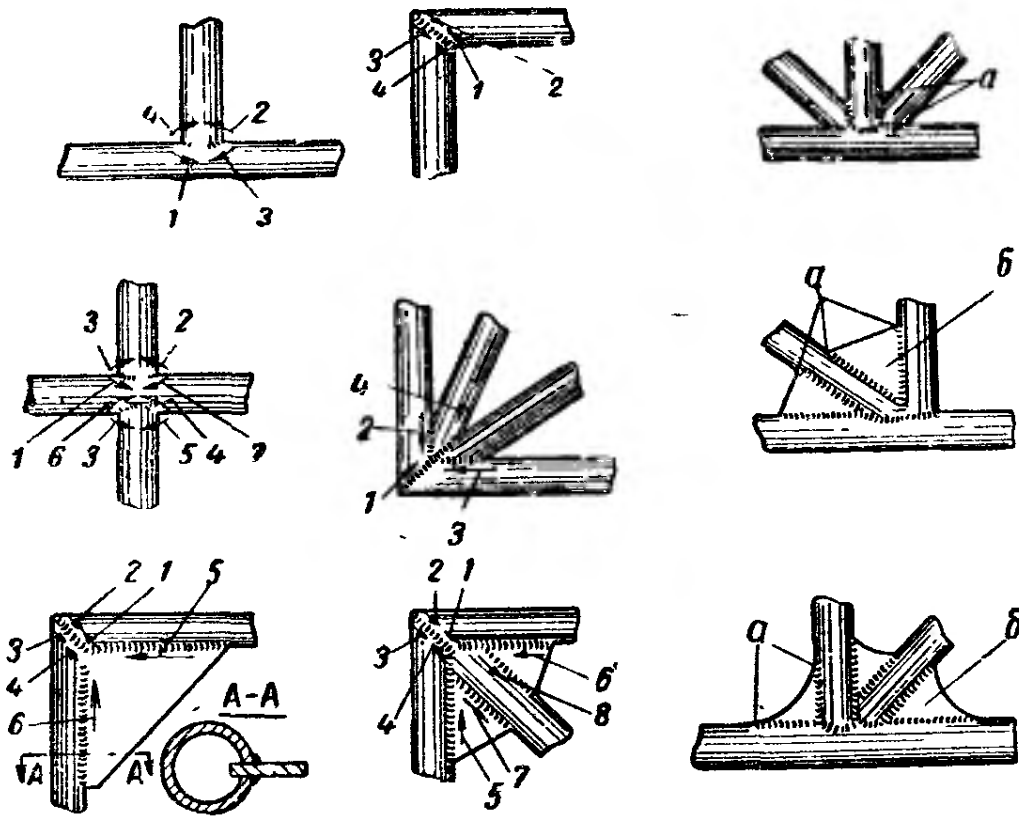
Типовые узлы трубчатых конструкций из хромокремнемарганцевой стали (цифры показывают порядок наложения швов, стрелки — направление сварки)
